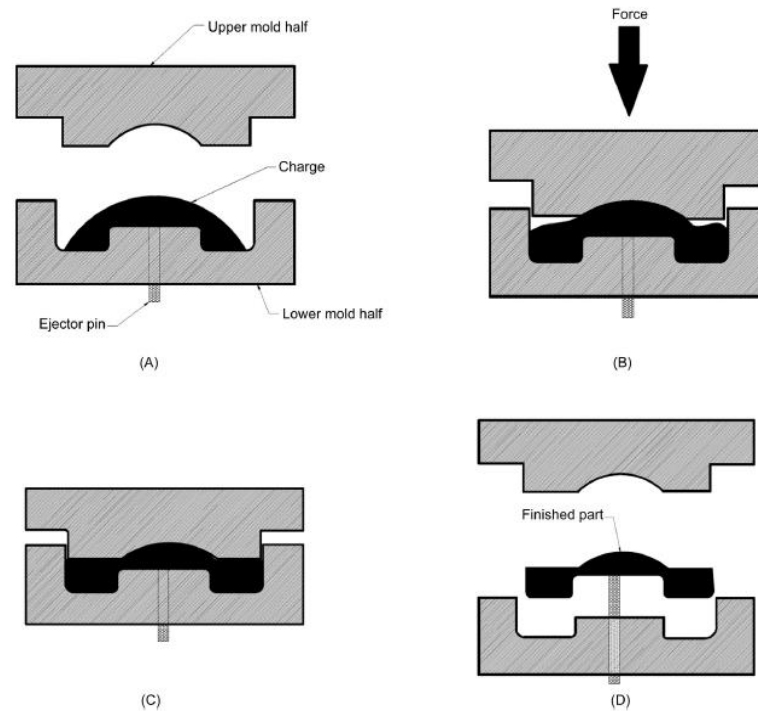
El proceso de moldeo por compresión descrito simplificado en cuatro pasos. (A) Cargado del compuesto en el molde. (B) Compactación del compuesto en molde caliente. (C) Curado de la pieza dentro de la cavidad del molde. (D) Expulsión de pieza [91].
